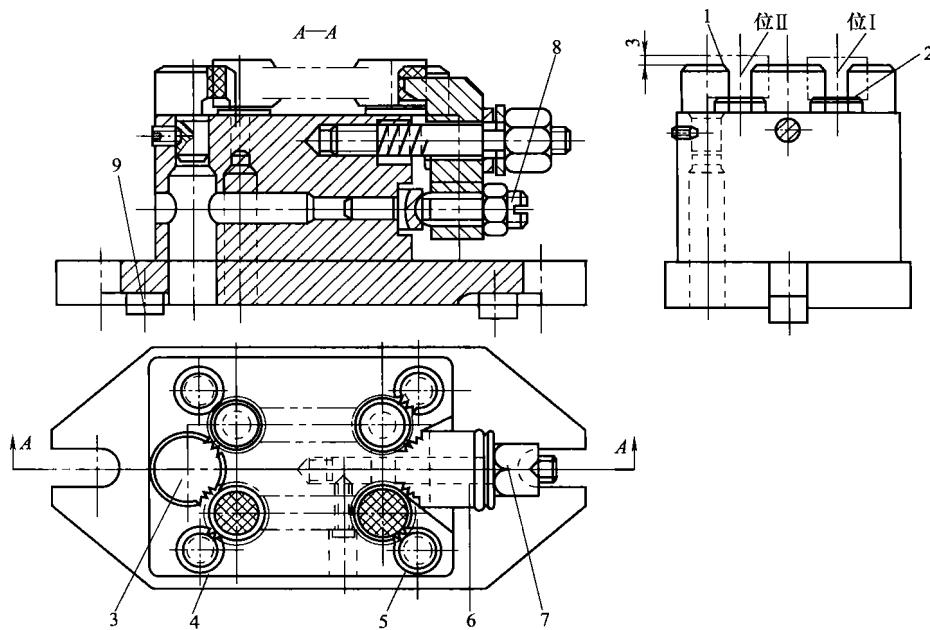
铣削连杆状零件两面的双位置专用铣床夹具
